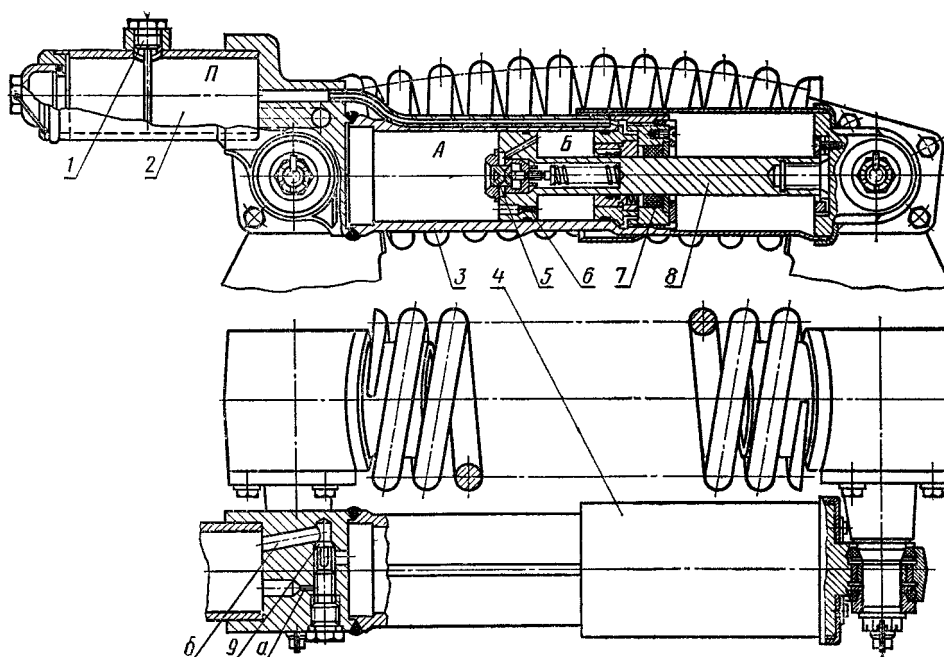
Гидроамортизатор балансирующей каретки подвески:
